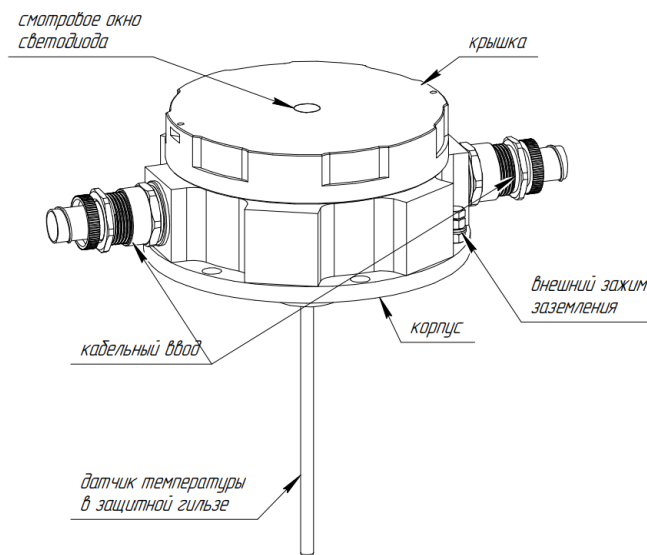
Внешний вид и элементы конструкции извещателя пожарного взрывозащищенного.
